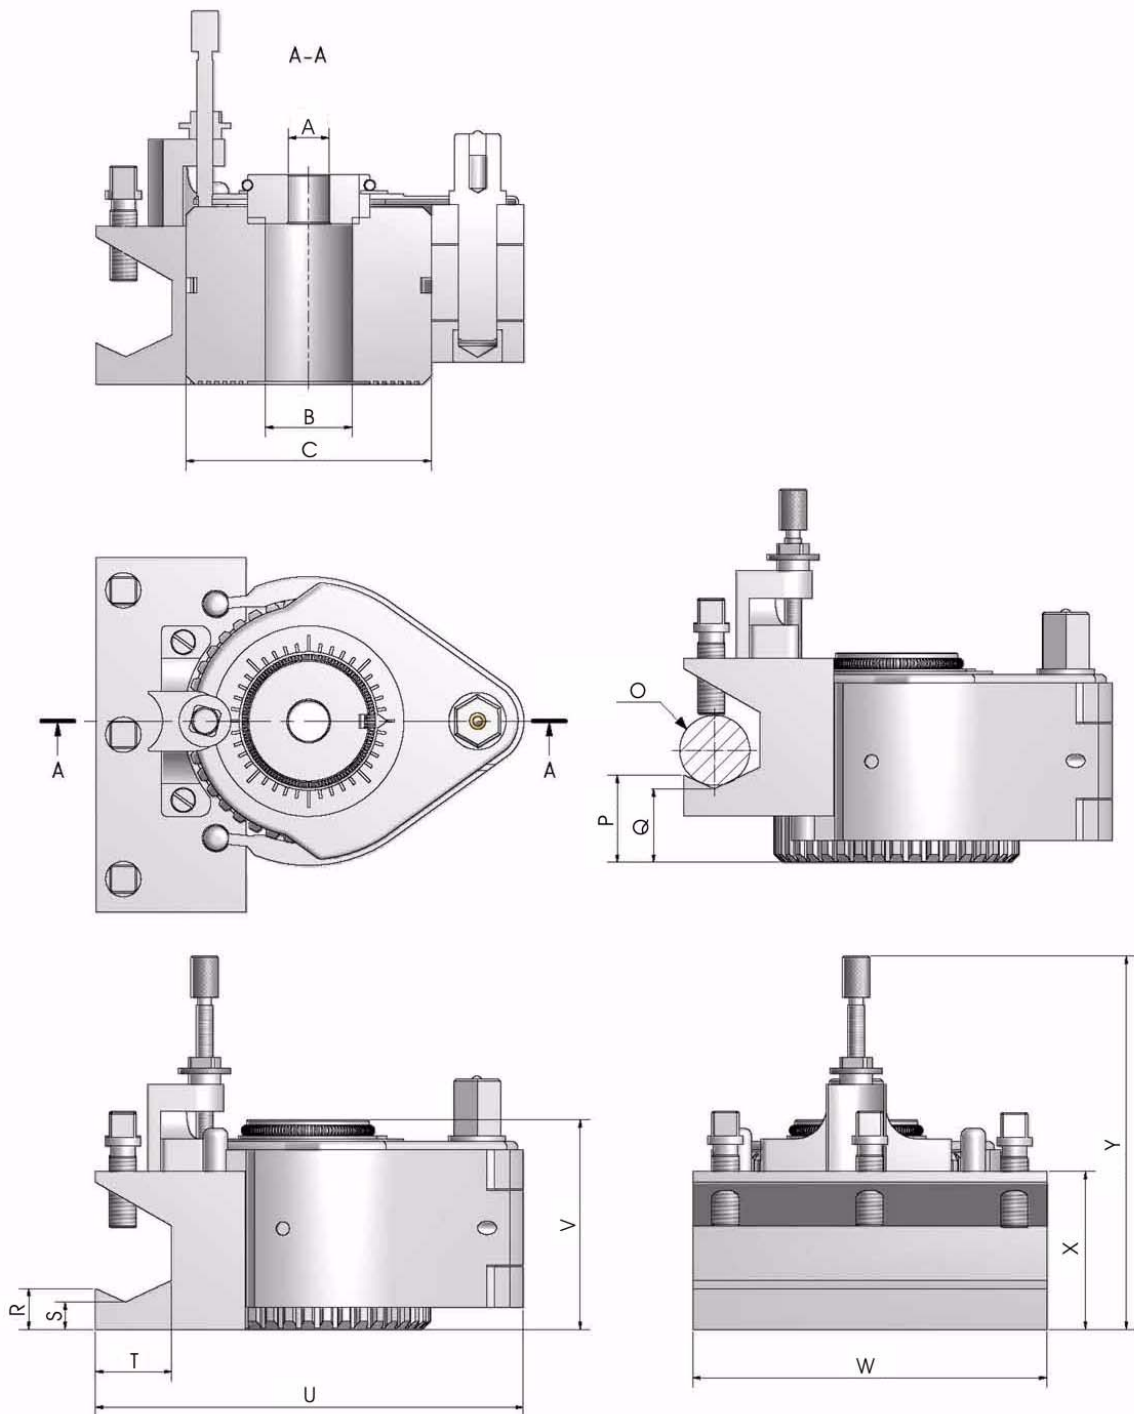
Stahlhalter für Rundmeißel - Tool holder for round tool
